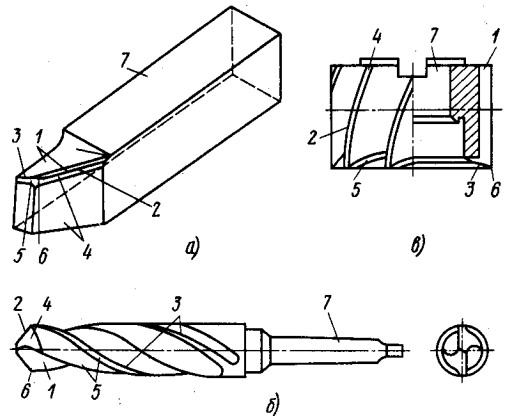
Геометрические и конструктивные элементы режущих инструментов: а — токарного резца; б — сверла; в — фрезы: 1 — передняя поверхность лезвия; 2 — главная режущая кромка; 3 — вспомогательная режущая кромка; 4 — главная задняя поверхность лезвия; 5 — вспомогательная задняя поверхность лезвия; 6 — вершина лезвия; 7 — крепежная часть инструмента
